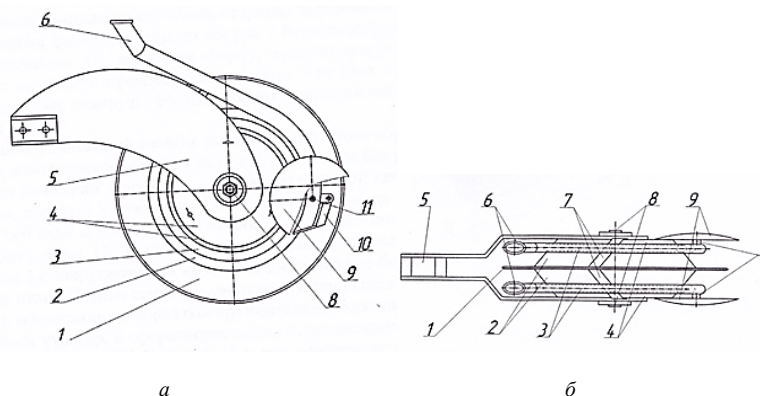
Комбинированный однодисковый сошник с двусторонними ребордами и сферическими дисковыми загортачами для узкорядного посева: *а* – вид сбоку; *б* – вид сверху; 1 – плоский диск; 2 и 4 – реборды; 3 – бороздкообразователи; 5 – корпус; 6 – семянаправители; 7 – чистик; 8 – ось; 9 – сферический диск; 10 – клапан; 11 – оси
